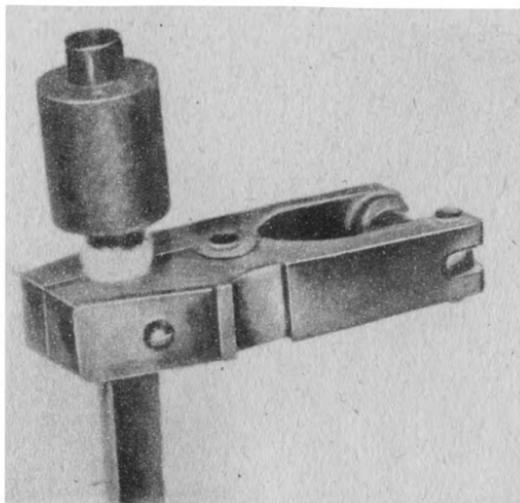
Патрон марки АС с охладителем, установленный для сварки алюминиевой жилы кабеля со стальным стержнем
